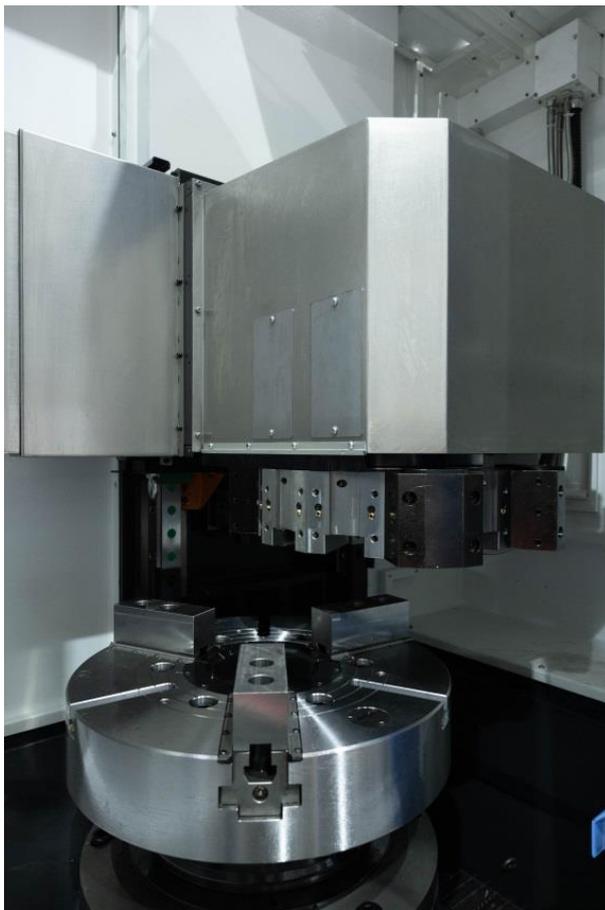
Револьверная головка токарного станка с ЧПУ KVT 60
